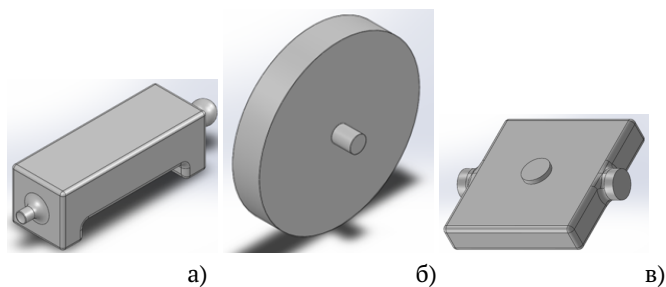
Компоненты МКР: а) корпус; б) колесо; в) платформа подвижной колесной пары
